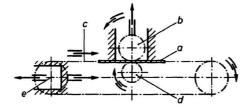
,1. Máquina de desbarbar (dibujo de conjunto)
